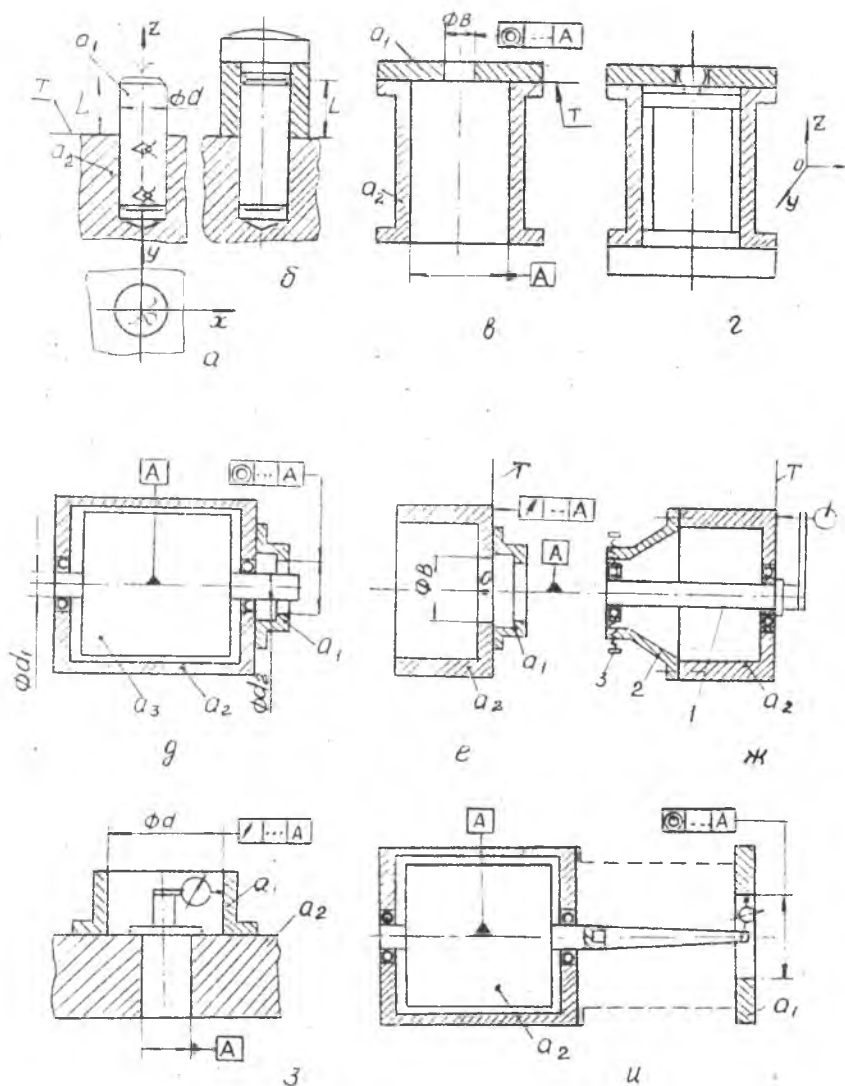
Примеры базирования элементов с помощью поверхностей изделия и сборочного приспособления
